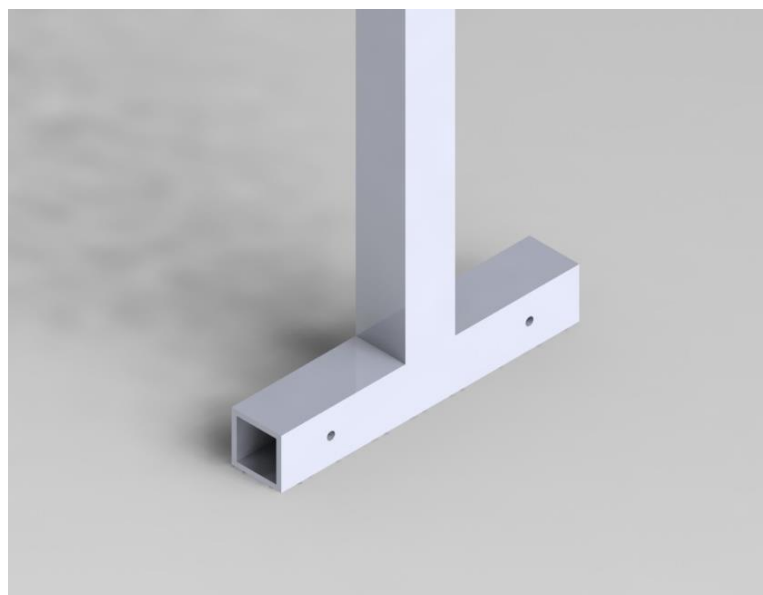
Ensamblaje subconjunto 1.5. Soldadura 1, 2, 3 y 4.
